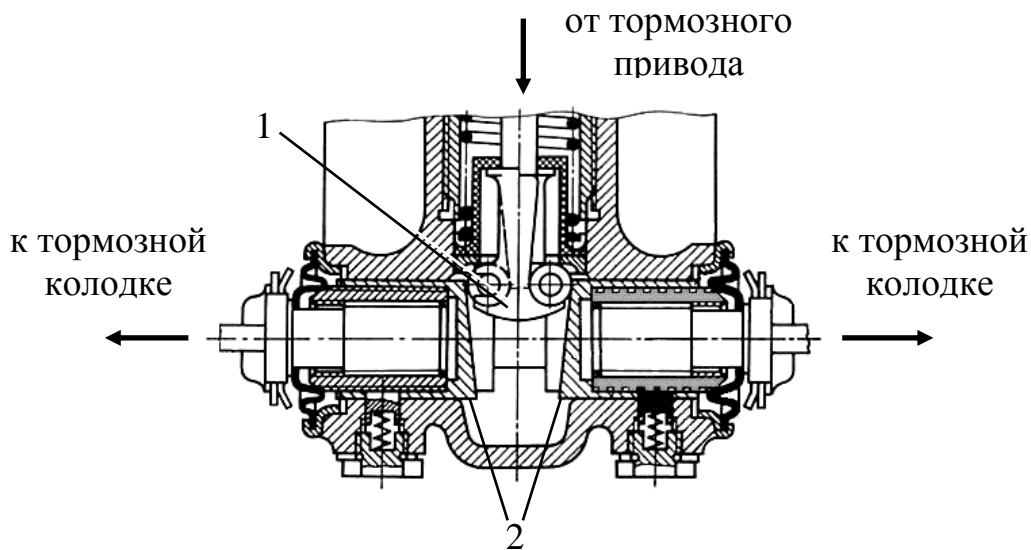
Конструкция клинового разжимного устройства барабанного тормозного механизма: 1 – клин; 2 – толкатели
